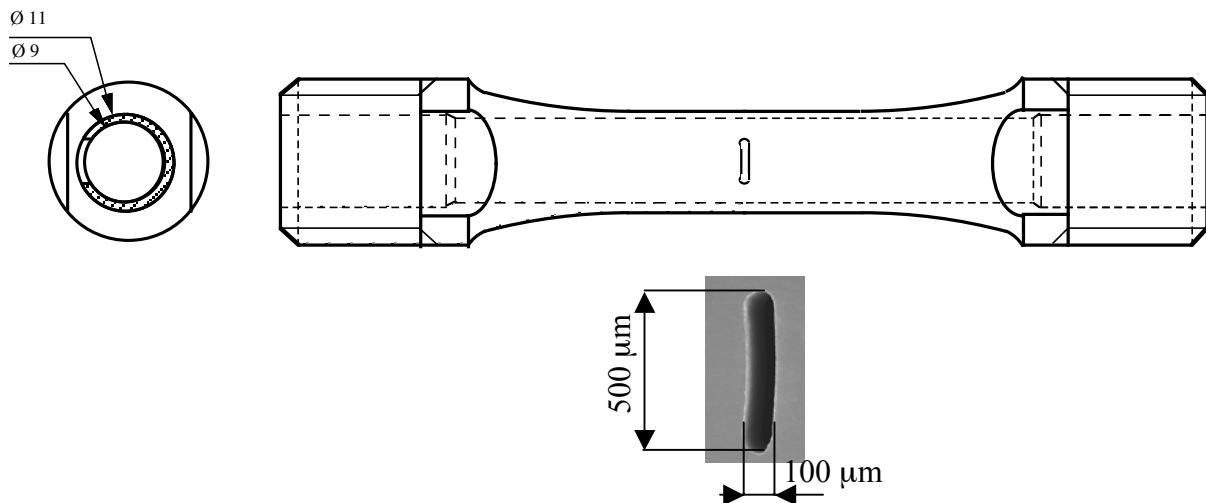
Géométrie et dimensions de l'entaille sur éprouvette tubulaire
